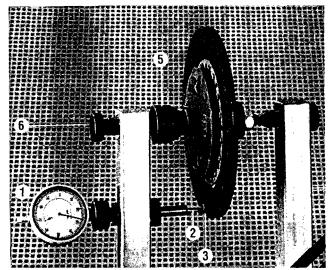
Проверка биения рабочей поверхности ведомого диска. 1 – стрелочный индикатор; 2 – выдвижной шток; 3 – щуп; 4 – шлицевой вал; 5 – крепёжный винт.
